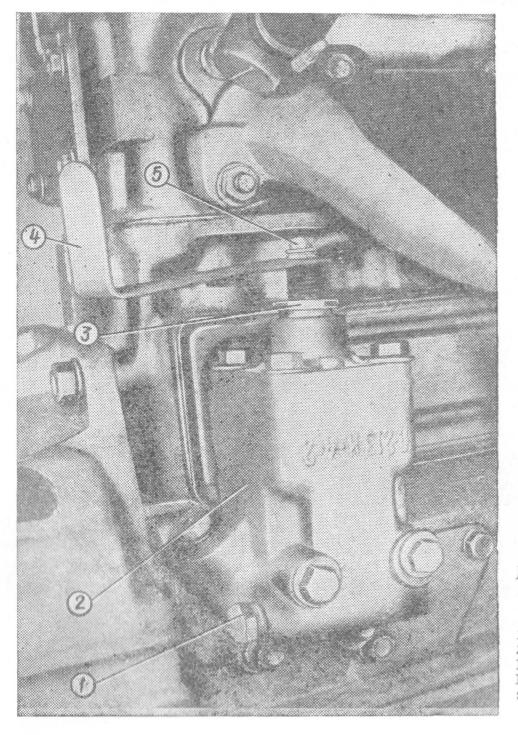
Lage des Hauptstromölfilters am Motor: 1 — Ablaßschraube;
